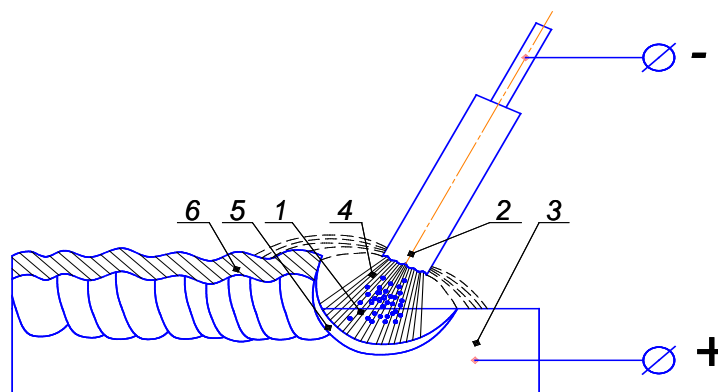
Ручная дуговая сварка покрытым электродом
